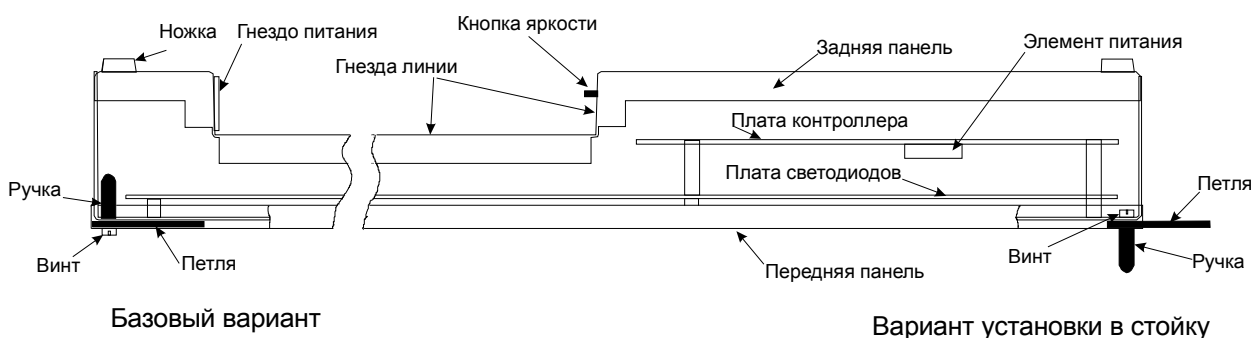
Табло ST 2U Wall со снятой верхней крышкой.
